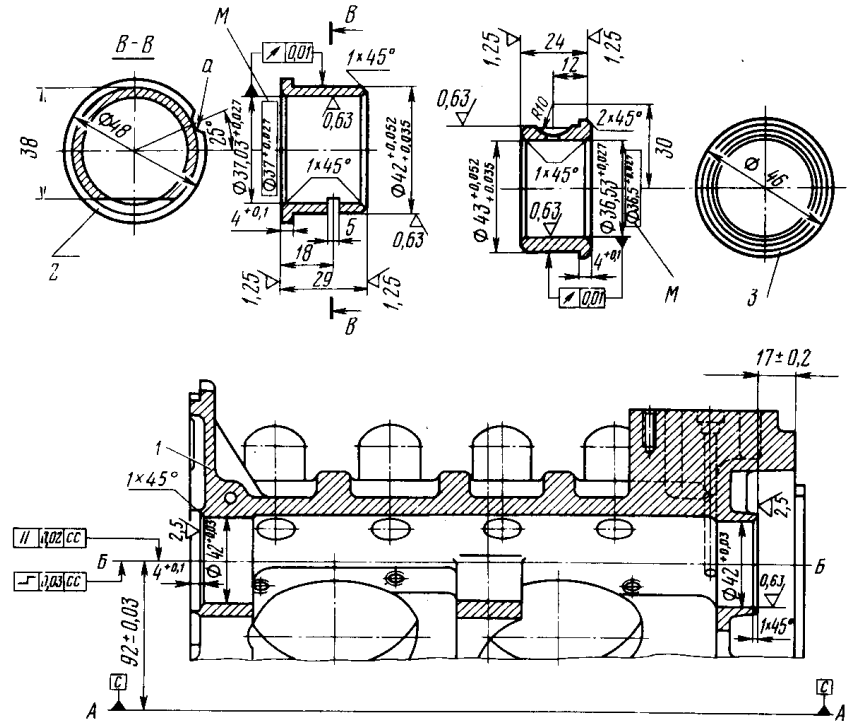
Расточка картера коленчатого вала под ремонтные подшипники распределительного вала:
